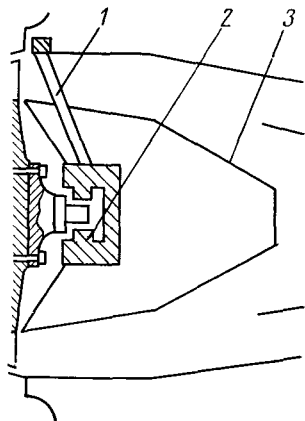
Схема крепления корпуса подшипника ГТУ «Базилиск» фирмы Бадворт:
